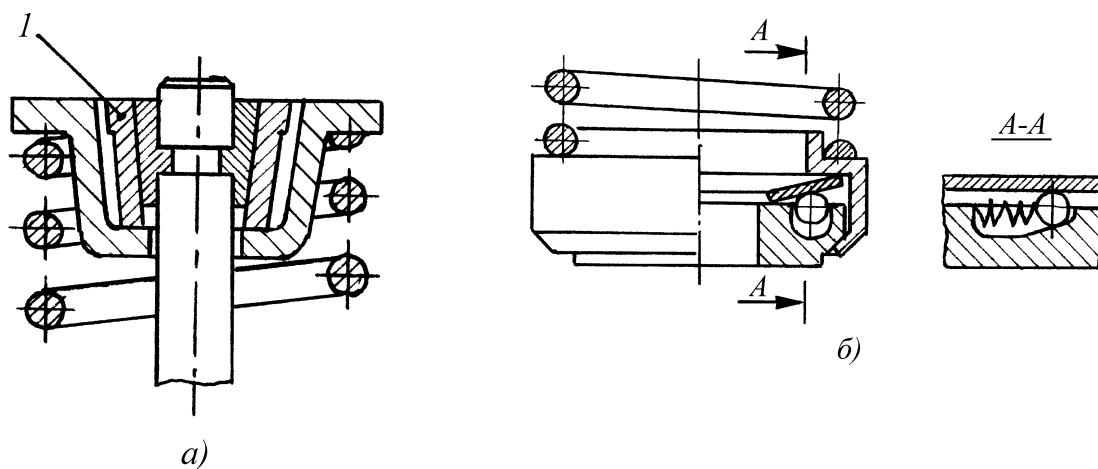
Устройства, обеспечивающие вращение клапана
